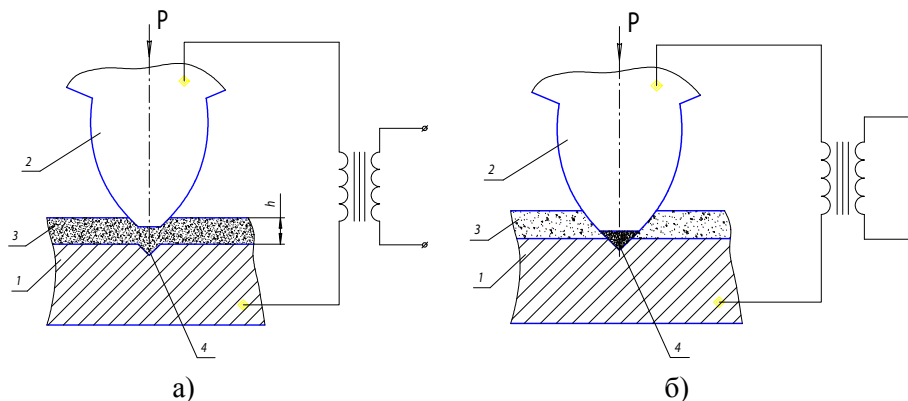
Установка для контактної наварювання на зношені вершини зубців шестерень (а) та принципова схема пристрою для автоматизації процесу наварювання (б)
